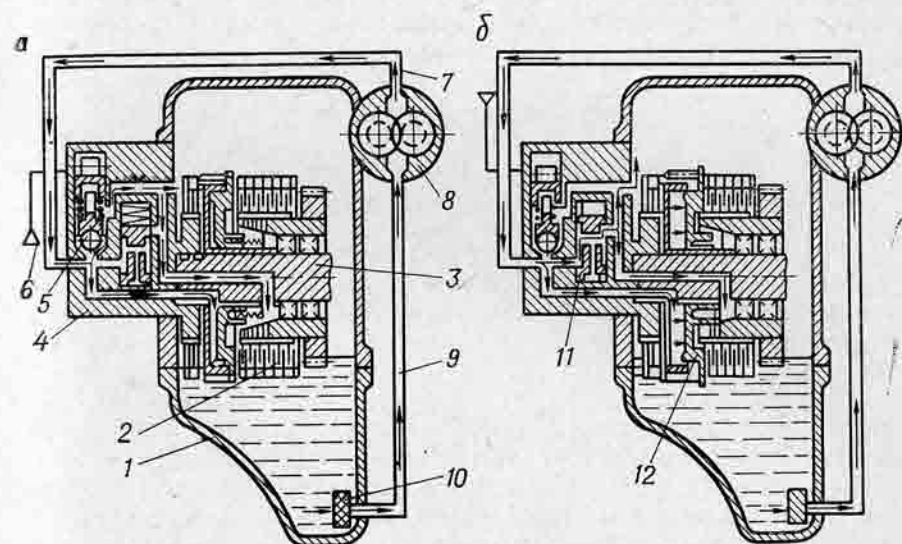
Схема взаимодействия элементов гидросистемы привода лебедки: а — гидроподжимная муфта выключена; б — гидроподжимная муфта включена; 1 — поддон редуктора; 2 — диски гидроподжимной муфты; 3 — вторичный вал; 4 — крышка с клапанами; 5 — клапан плавного включения; 6 — рычаг; 7 — нагнетающий маслопровод; 8 — насос; 9 — всасывающий маслопровод; 10 — сетчатый фильтр; 11 — перепускной клапан; 12 — поршень
